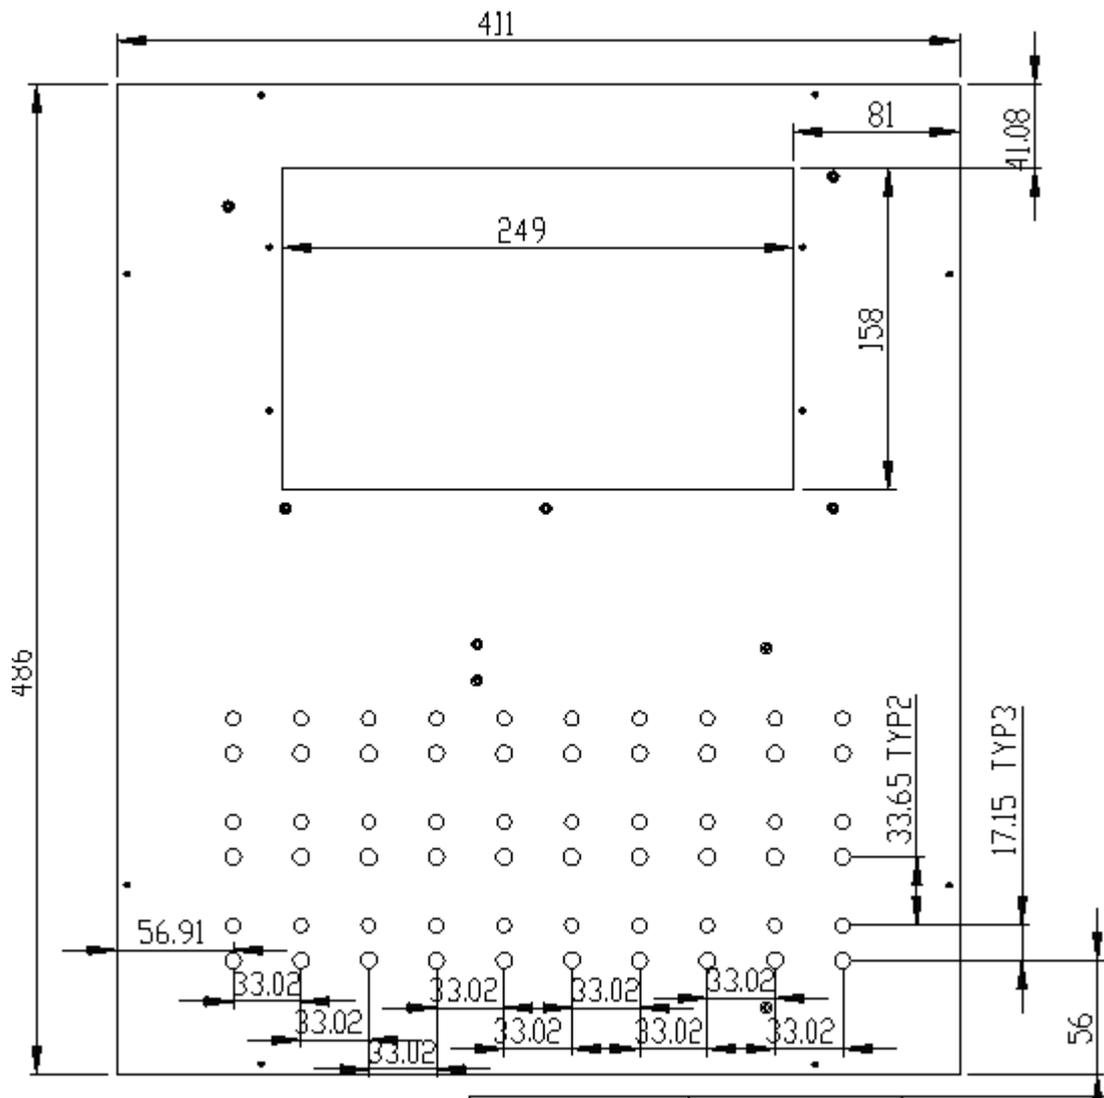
Platinum Touch 30 Dimensões do Painel Frontal
